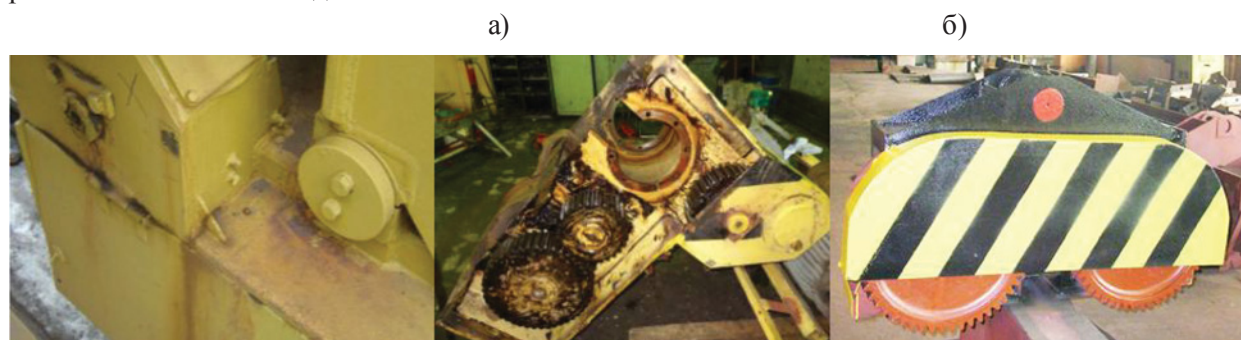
Конструкции защиты зубчатых передач от загрязнений:
